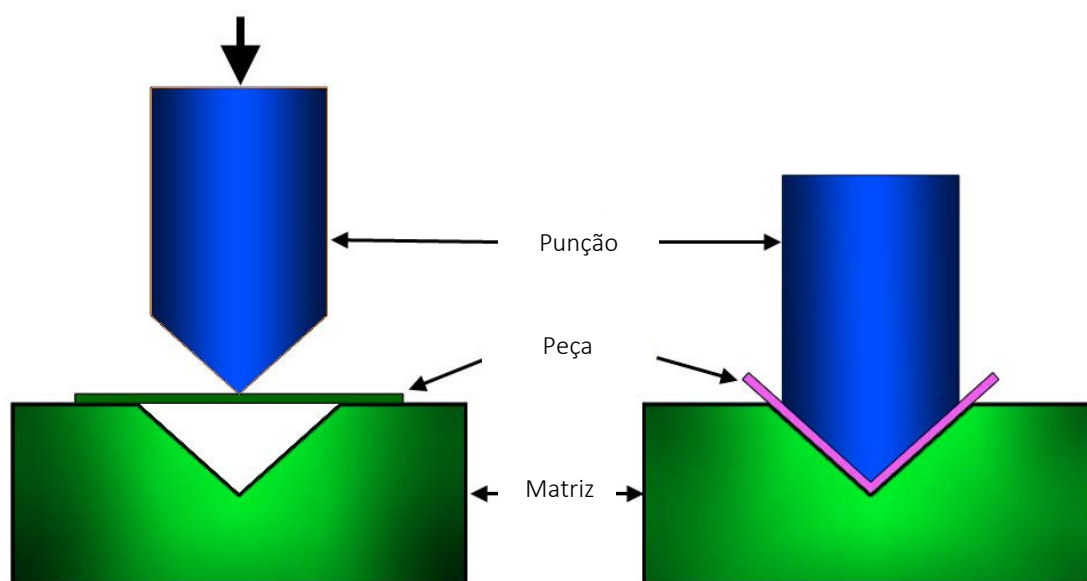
Princípio do processo de Quinagem ¹⁸
